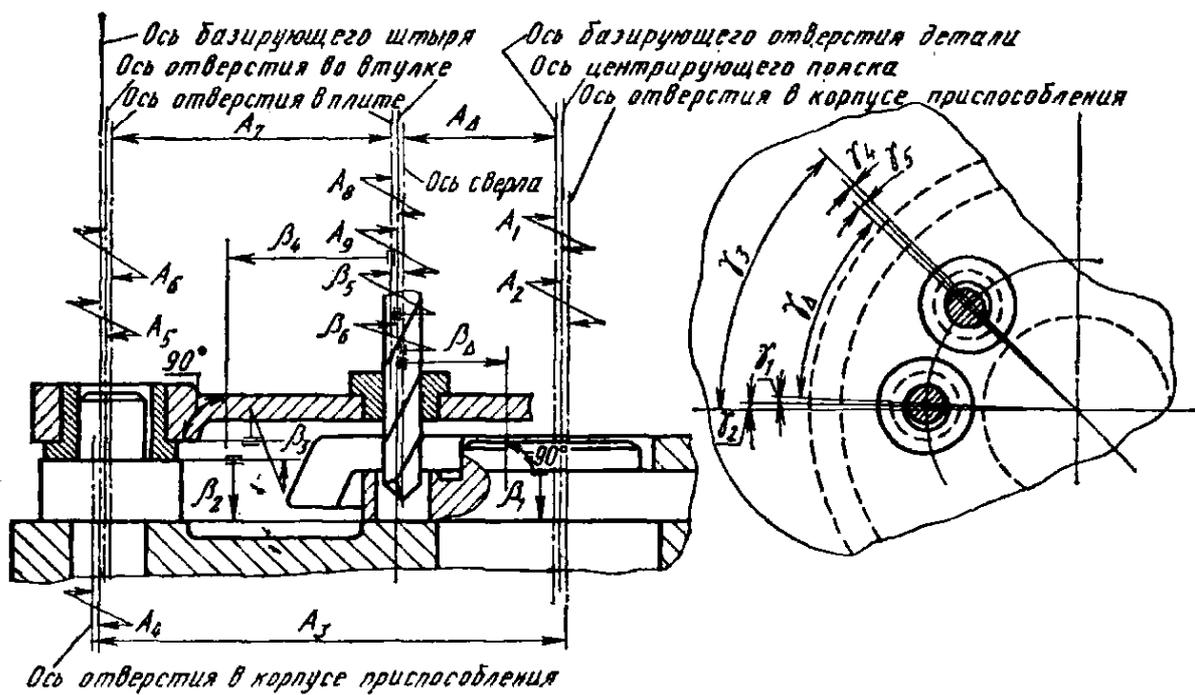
Схема размерных цепей системы станок-приспособление-инструмент-заготовка агрегатного станка, с помощью которых достигается точность положения одного из обрабатываемых отверстий
